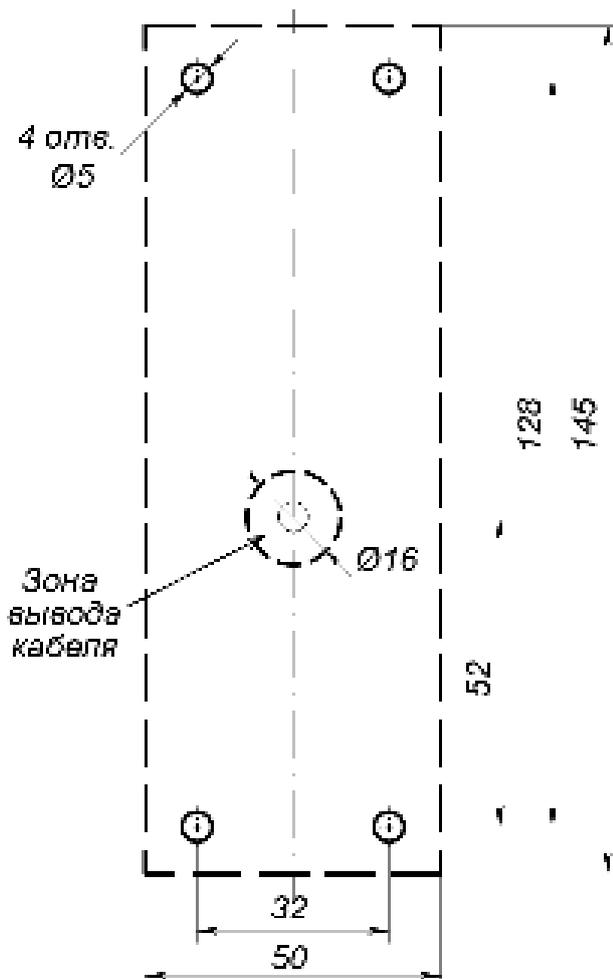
Схема разметки отверстий для установки считывателя (пунктиром показаны габариты корпуса считывателя)
